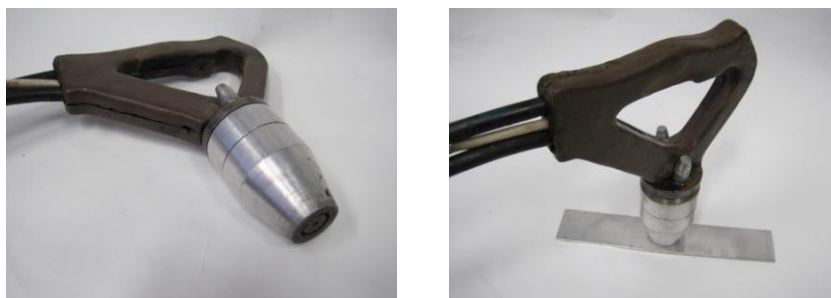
Плазмотрон для ручной сварки 3-х фазной сжатой дугой
